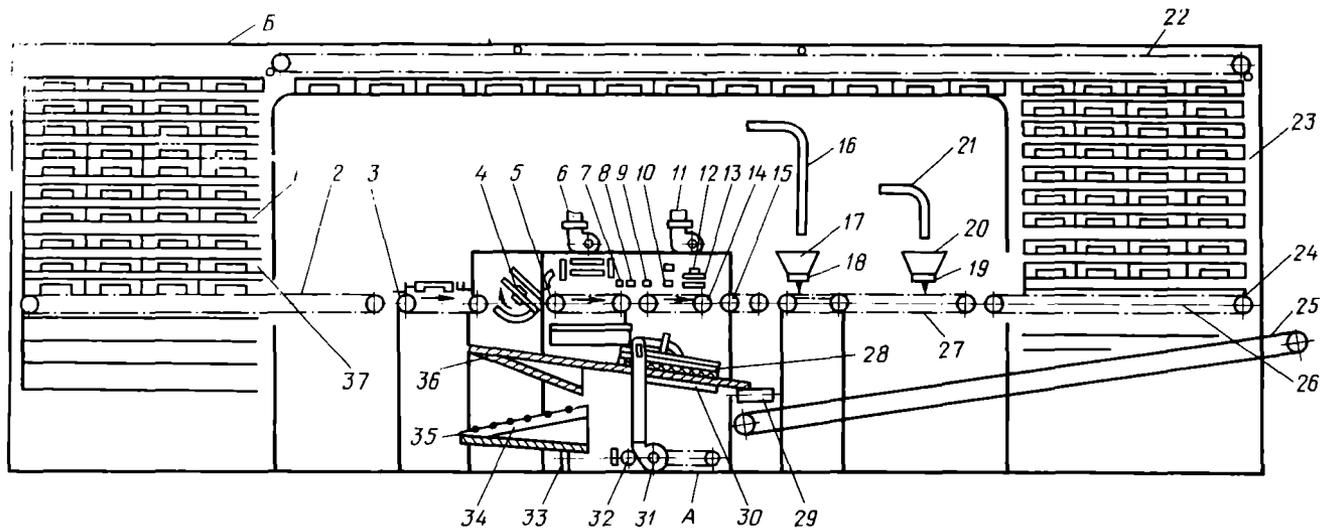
Схема поточной линии для отливки конфетных масс
